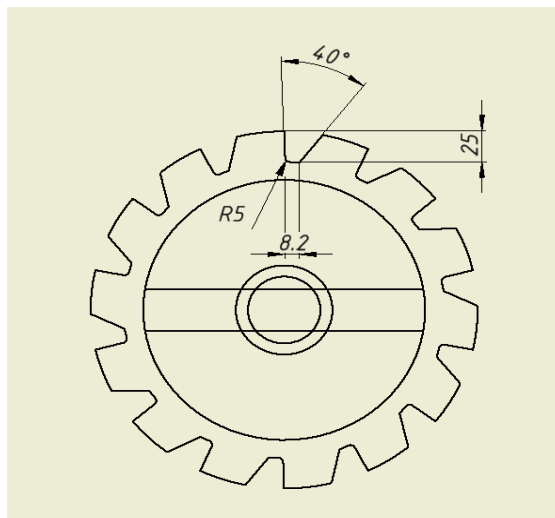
Ескіз корпусу фрези з канавками
